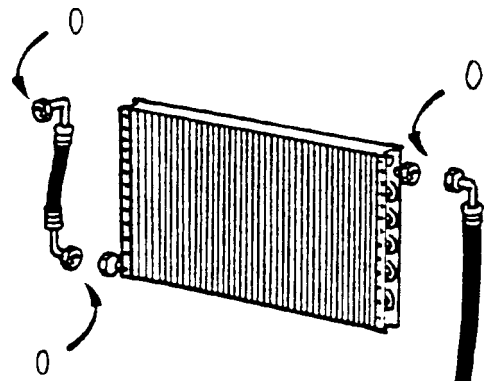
Austausch der alten R12 O-Ringe gegen neue R134a O-Ringe
